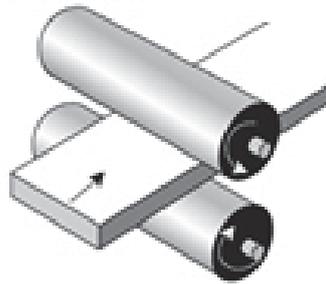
Cilindros para laminação de planos. (Fonte: Autor).
